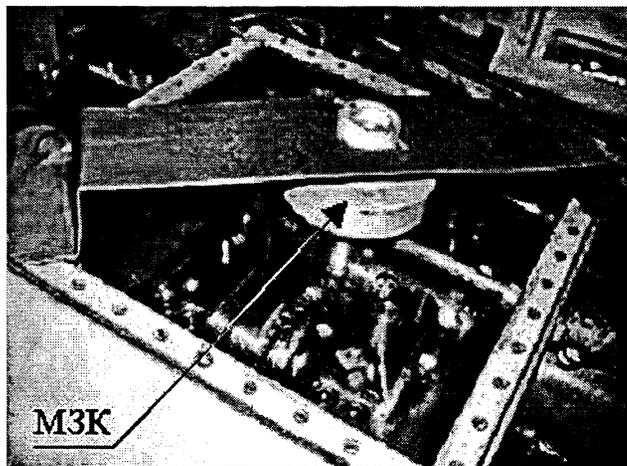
МЗК для контроля шума на стенде ИМИНМАШ НАН Беларуси для испытаний зубчатых передач
